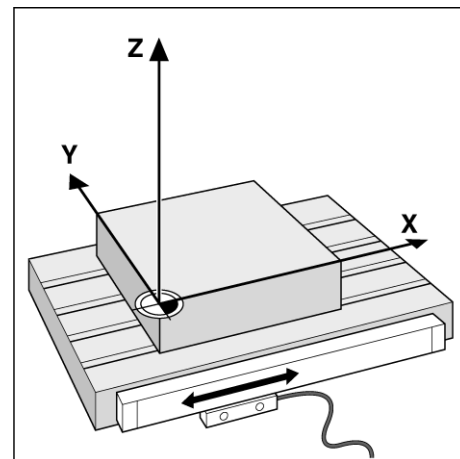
Positionsmessgerät für eine Linearachse, z.B. für die X-Achse
